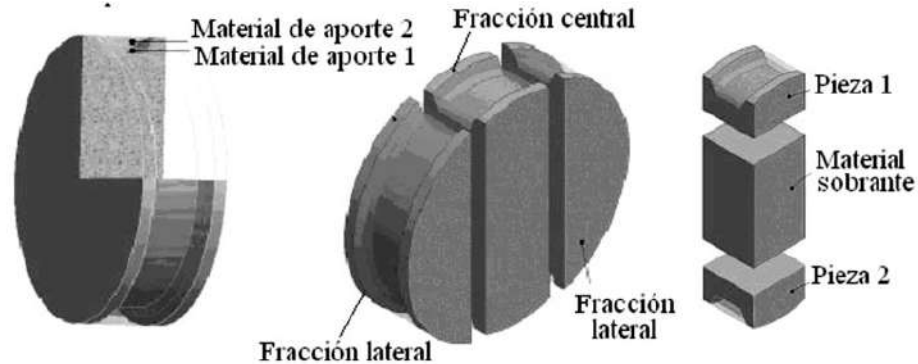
Vista en 3D de los cortes principales, secundarios y cortes de las fracciones laterales
